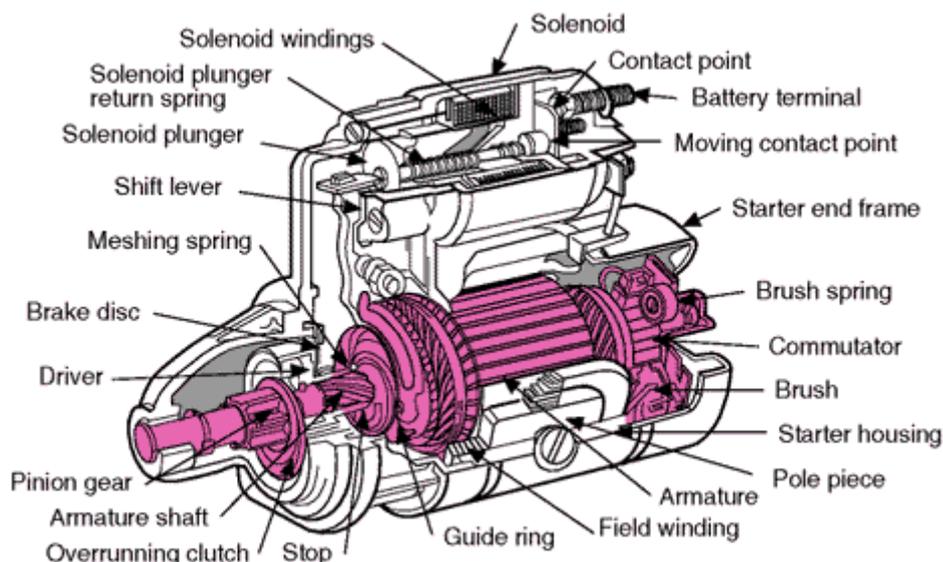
Elementos constituintes do motor de arranque - 1 ([7])
